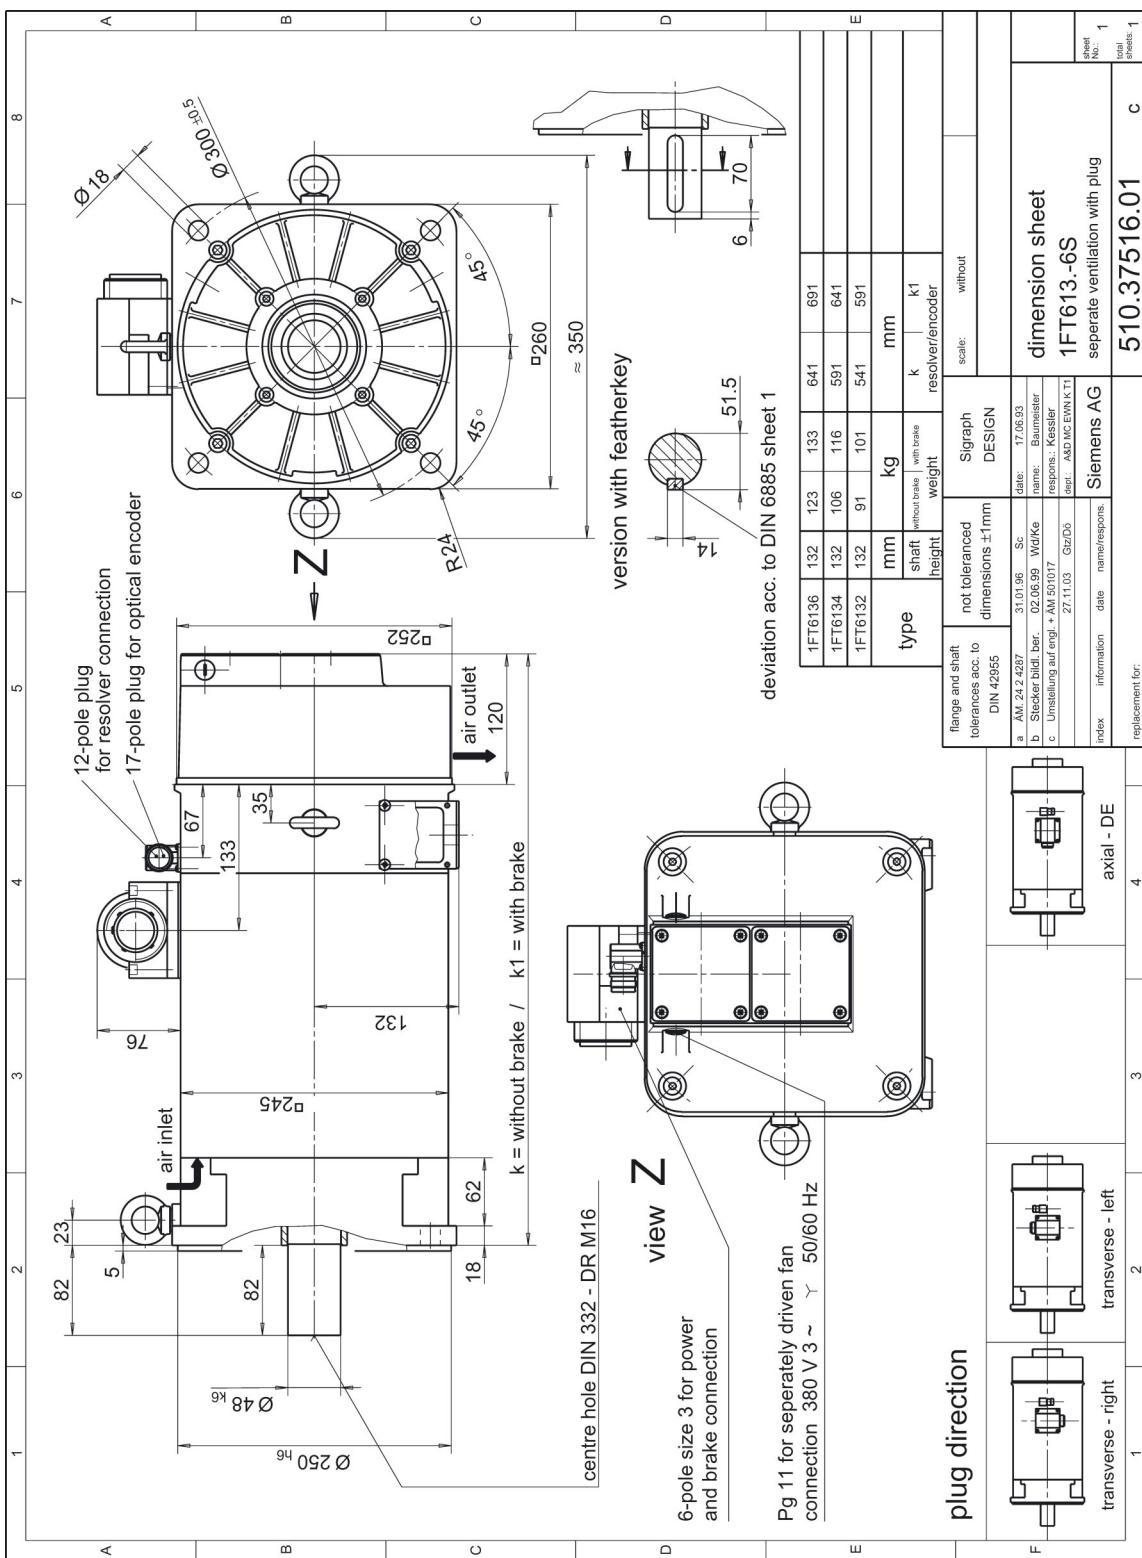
1FT613□ fremdbelüftet mit Stecker
